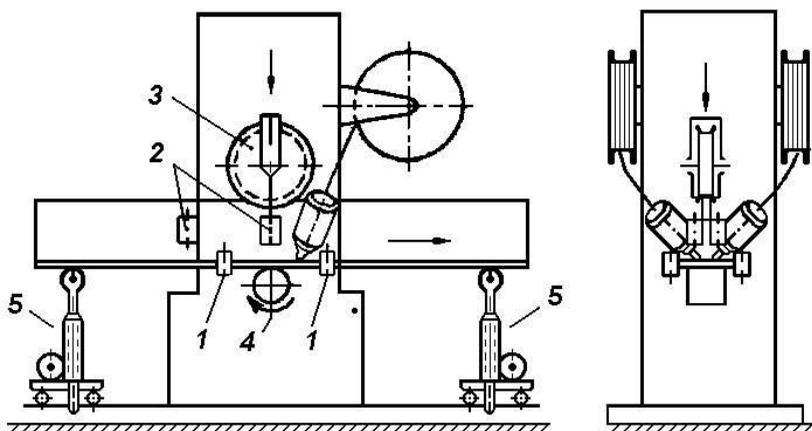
Станок-автомат для сварки тавровых балок.
